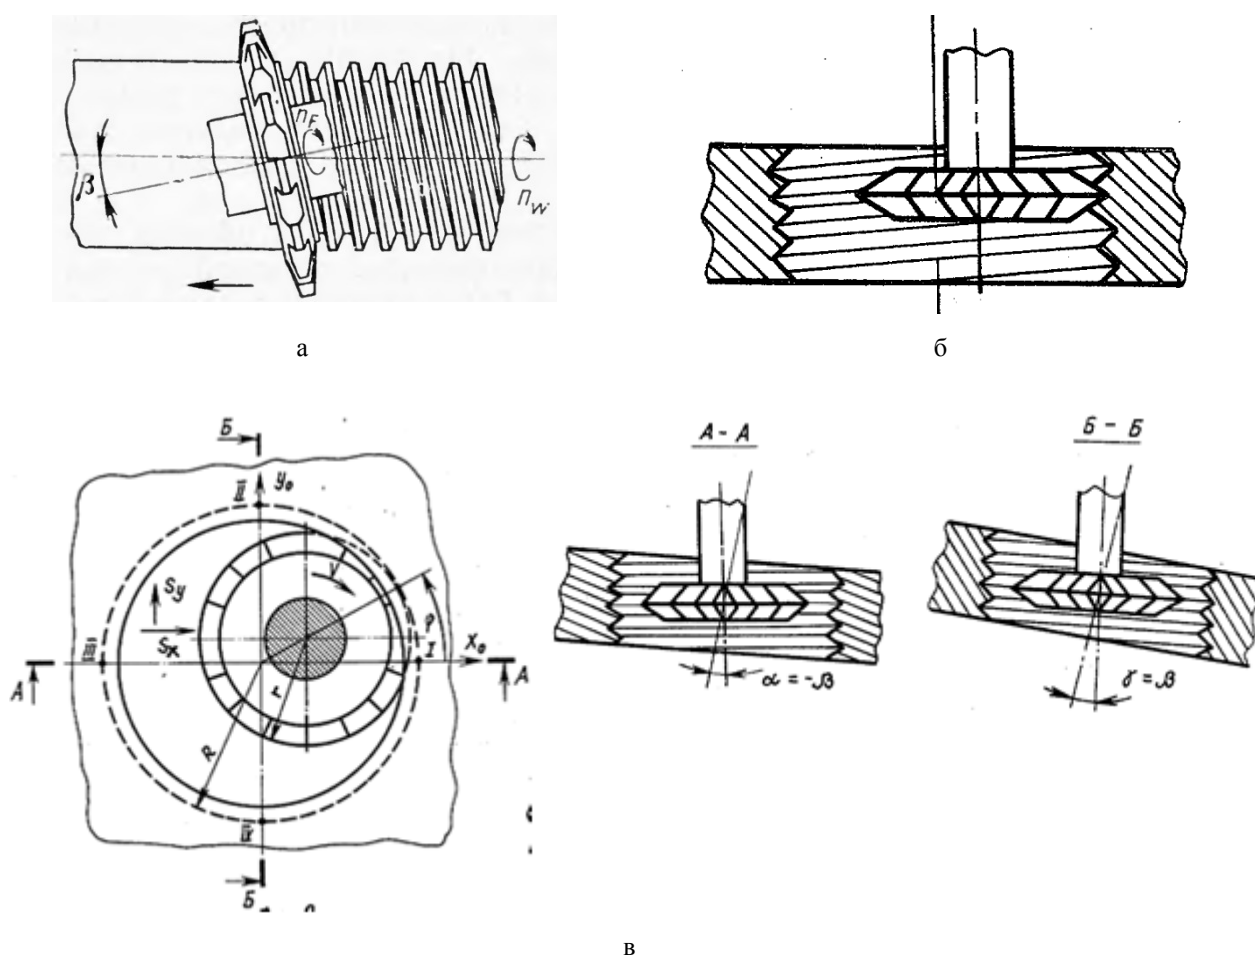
Фрезерование резьбы дисковой фрезой: а - фрезерование наружной резьбы, б,в - фрезерование внутренней резьбы.
